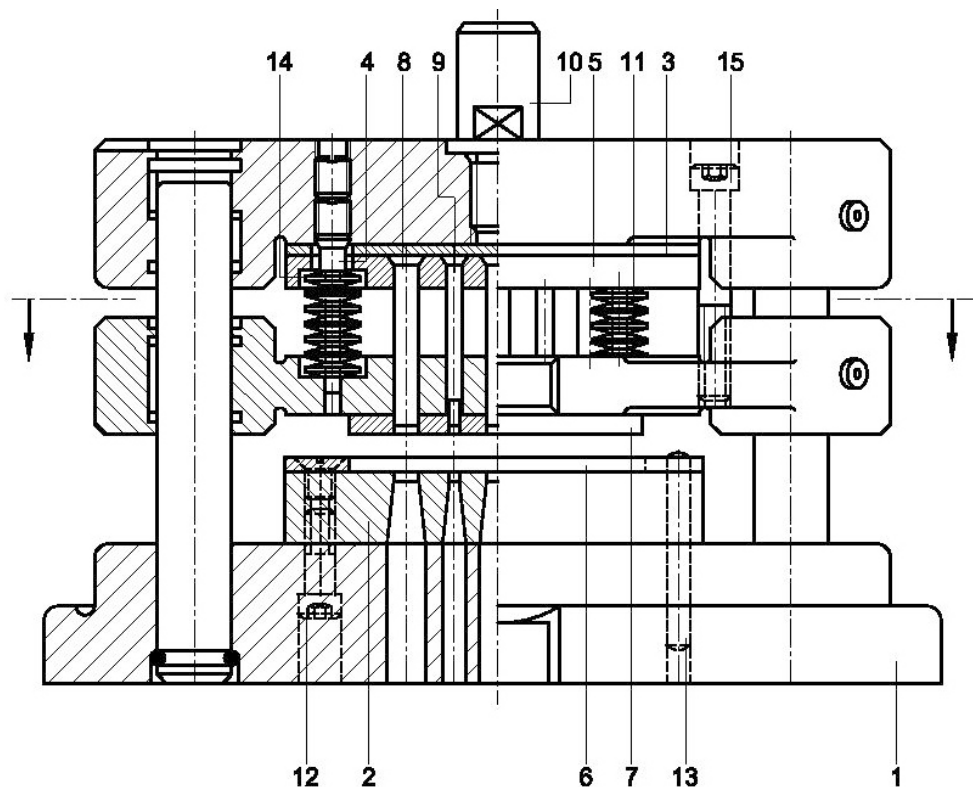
Säulenführungsschnitt mit Mehrfachloch
